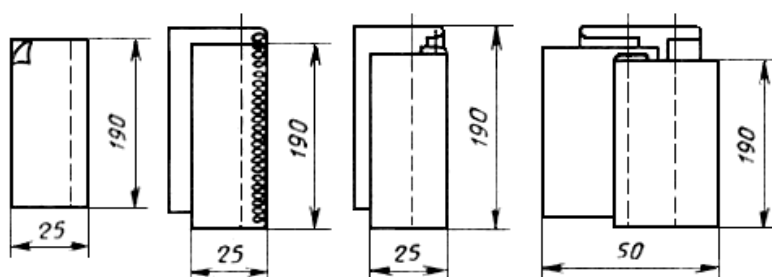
Схема изготовления проб для испытаний при приложении растягивающей нагрузки вдоль строчки
